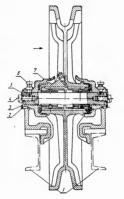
Схема регулировки направляющих колее тракторов КД-35, КДП-35 и Т-28: 1-швеллеры еусеничкой тележки; 2-регулировогом мые проклабжи; 3-упорная шайба; 4-болт упорной шайбы; 5-тамковая шайба; 6-устамоочный болт кориштейма; темроитейм колеса.
